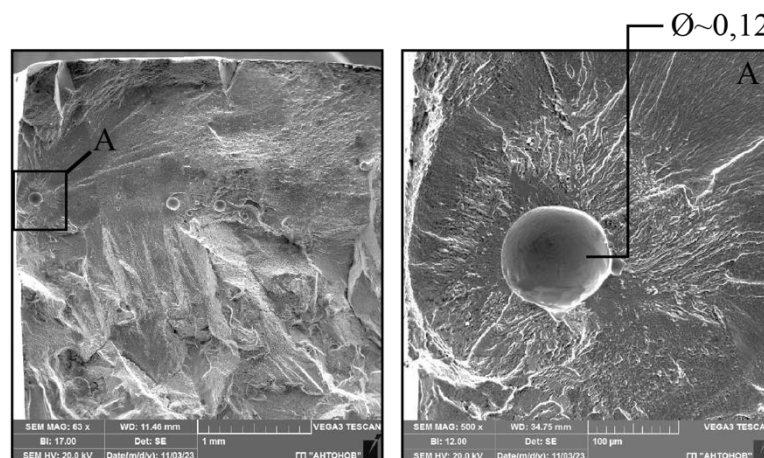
Вид пори в осередку тріщини зразка 4, яка розвинулась в наплавленому шарі справа від поверхні центрального отвору.
